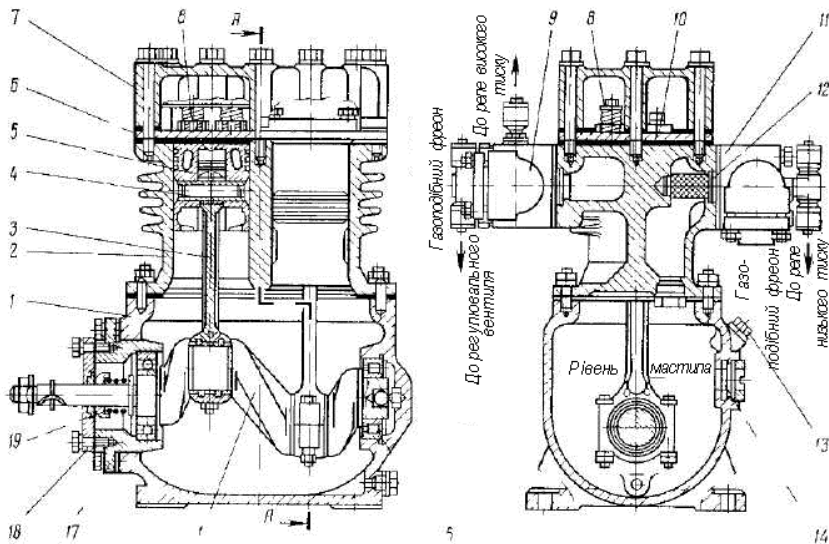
Поздовжній і поперечний розрізи поршневого компресора: 1 – картер; 2 – блок циліндрів; 3 – шатун; 4 – поршневий палець; 5 – поршень; 6 – клапанна дошка; 7 – голівка блоку циліндрів; 8 – нагнітальний клапан; 9 – нагнітальний запірний вентиль; 10 – всмоктувальний клапан; 11 – всмоктувальний запірний вентиль; 12 – фільтр; 13 – пробка заливання мастила; 14 – мастилопоказчик; 15 – корінні підшипники; 16 – колінвал; 17 – корпус підшипника; 18 – кришка сальника; 19 – сальник
